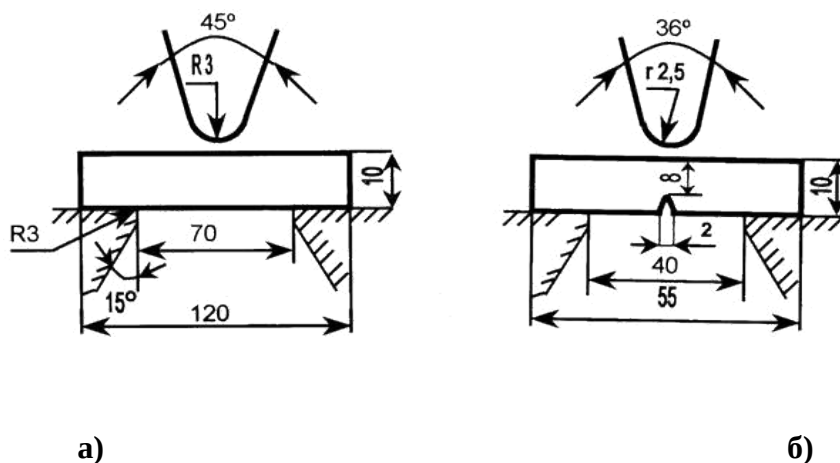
Образец с U-образным надрезом для испытаний на ударный изгиб
